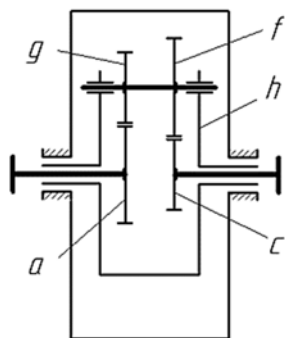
Планетарный редуктор с двухвенцовым сателлитом
